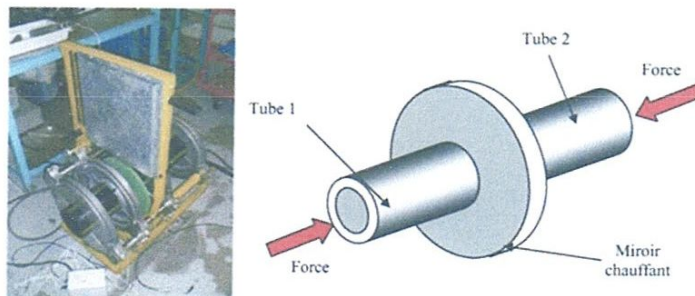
Chauffage des tubes lors du soudage bout à bout.
